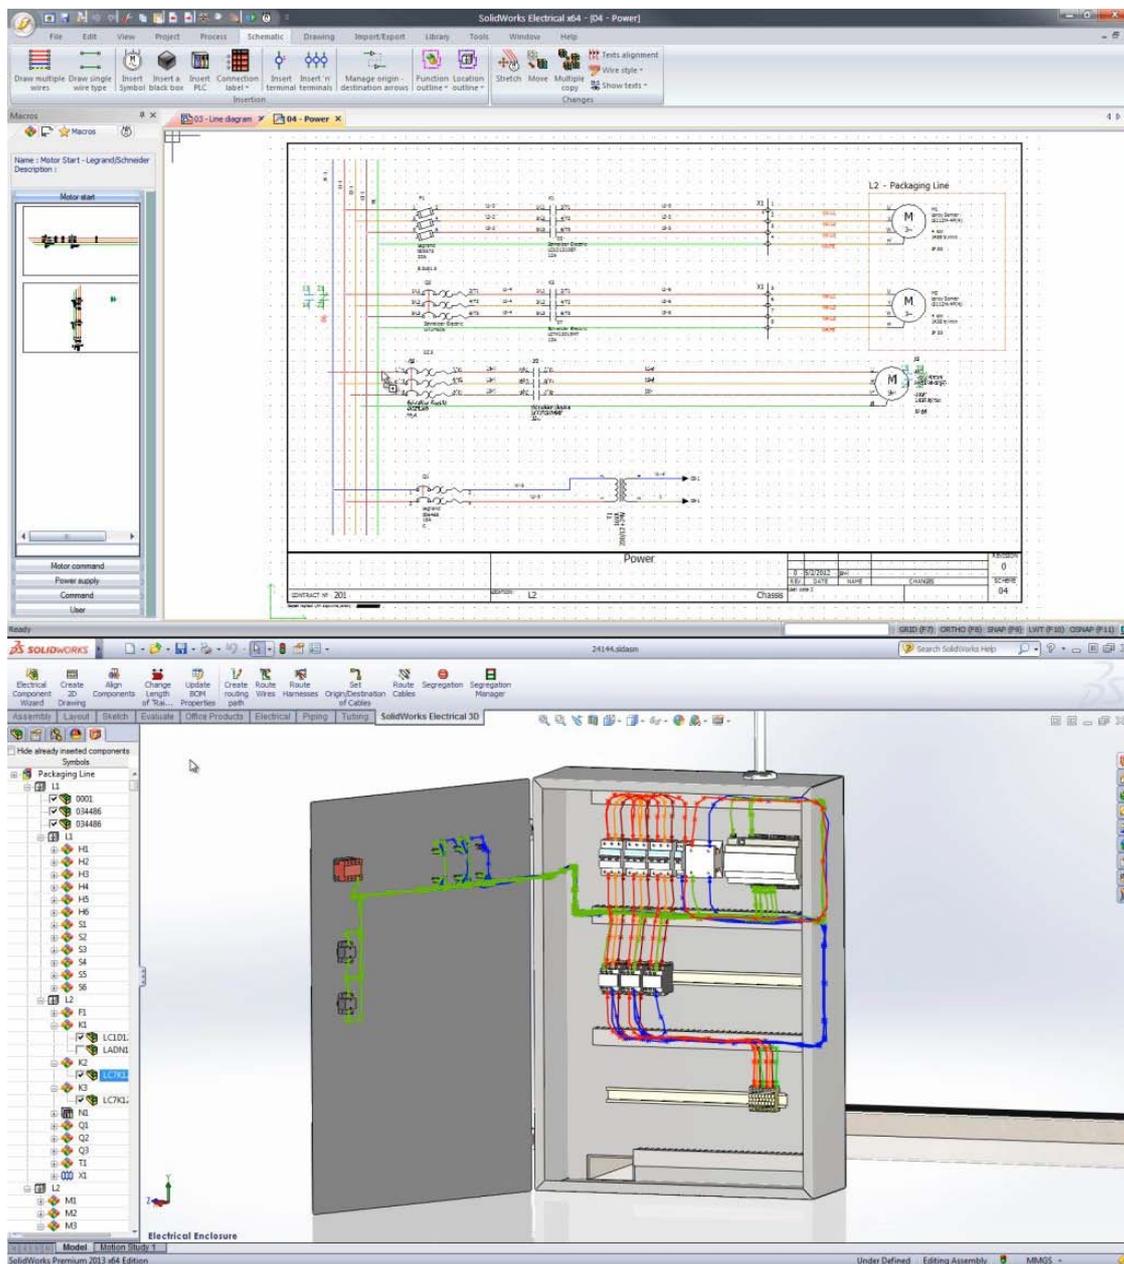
От схемы до сборки шкафа с SolidWorks Electrical.
